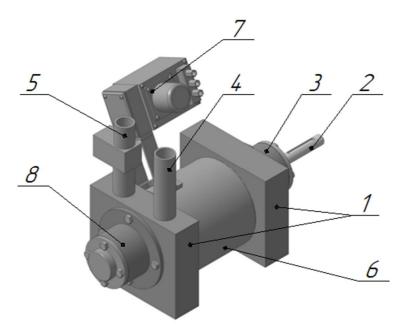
Одноступенчатый ЖВН с устройством автоматического регулирования нагнетательного окна: 1 – крышки; 2 – вал; 3 – подшипниковая опора; 4 – впускной патрубок; 5 – выпускной патрубок; 6 – корпус; 7 – нагнетательное устройство; 8 – подшипниковая опора
